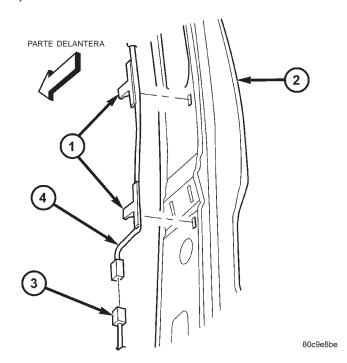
Desmontaje e instalación de cable de conexión flexible de airbag de cortina lateral
